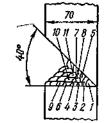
Порядок наложения швов при сварке горизонтального шва.
